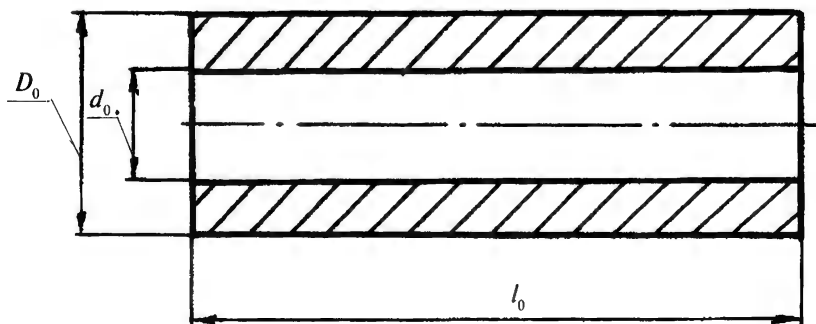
Схема к расчету размеров цилиндрической полый заготовки
